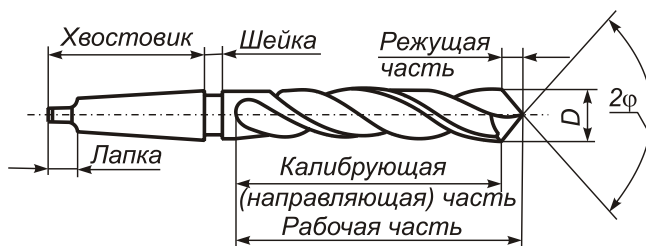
Общий вид и основные элементы конструкции винтового сверла
